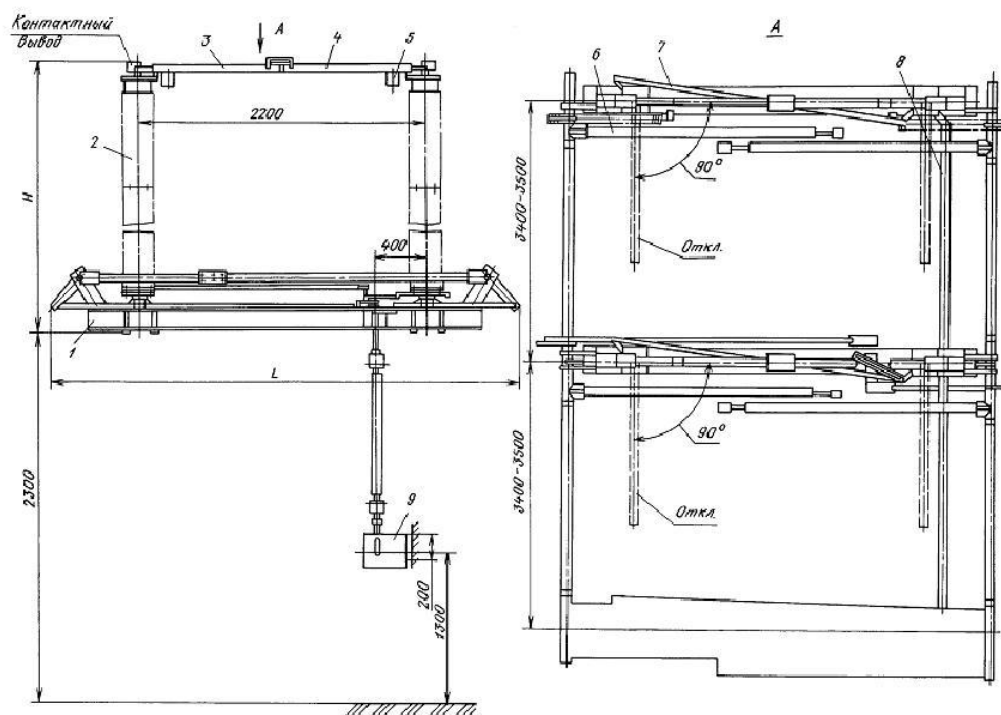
Внешний вид и габаритные размеры разъединителя РДЗ-110-П
